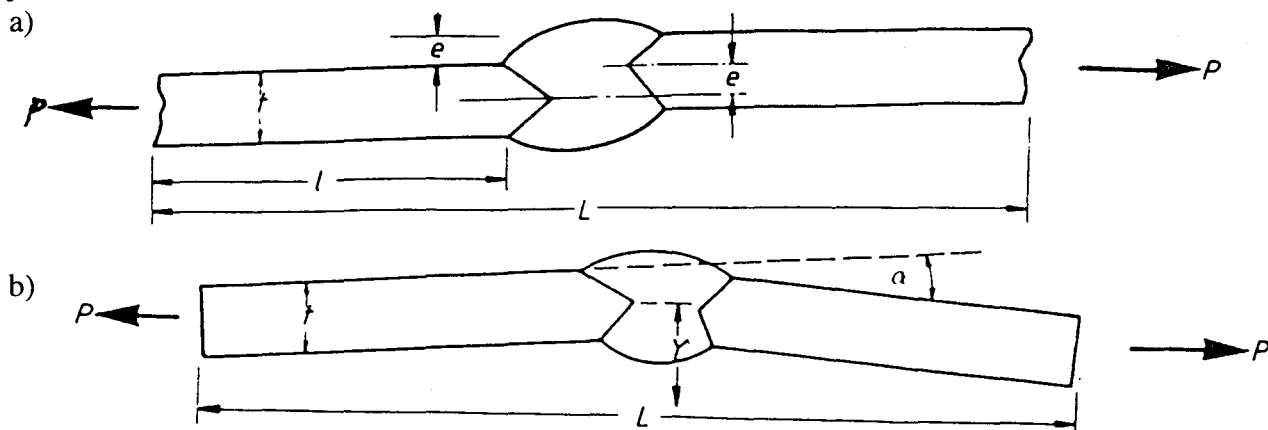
Désalignements axial (a) et angulaire (b) d'un joint soudé bout-à-bout [MAD85]
